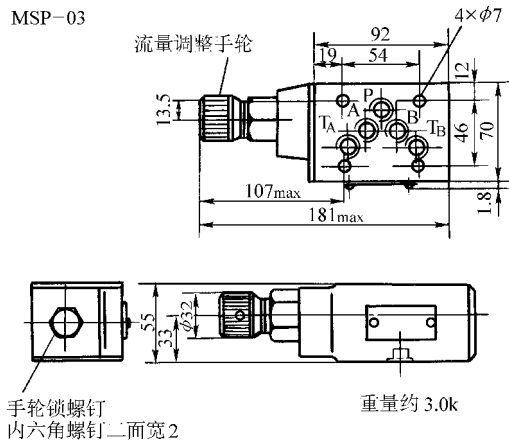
MSP-03 型叠加式节流阀的外形尺寸
